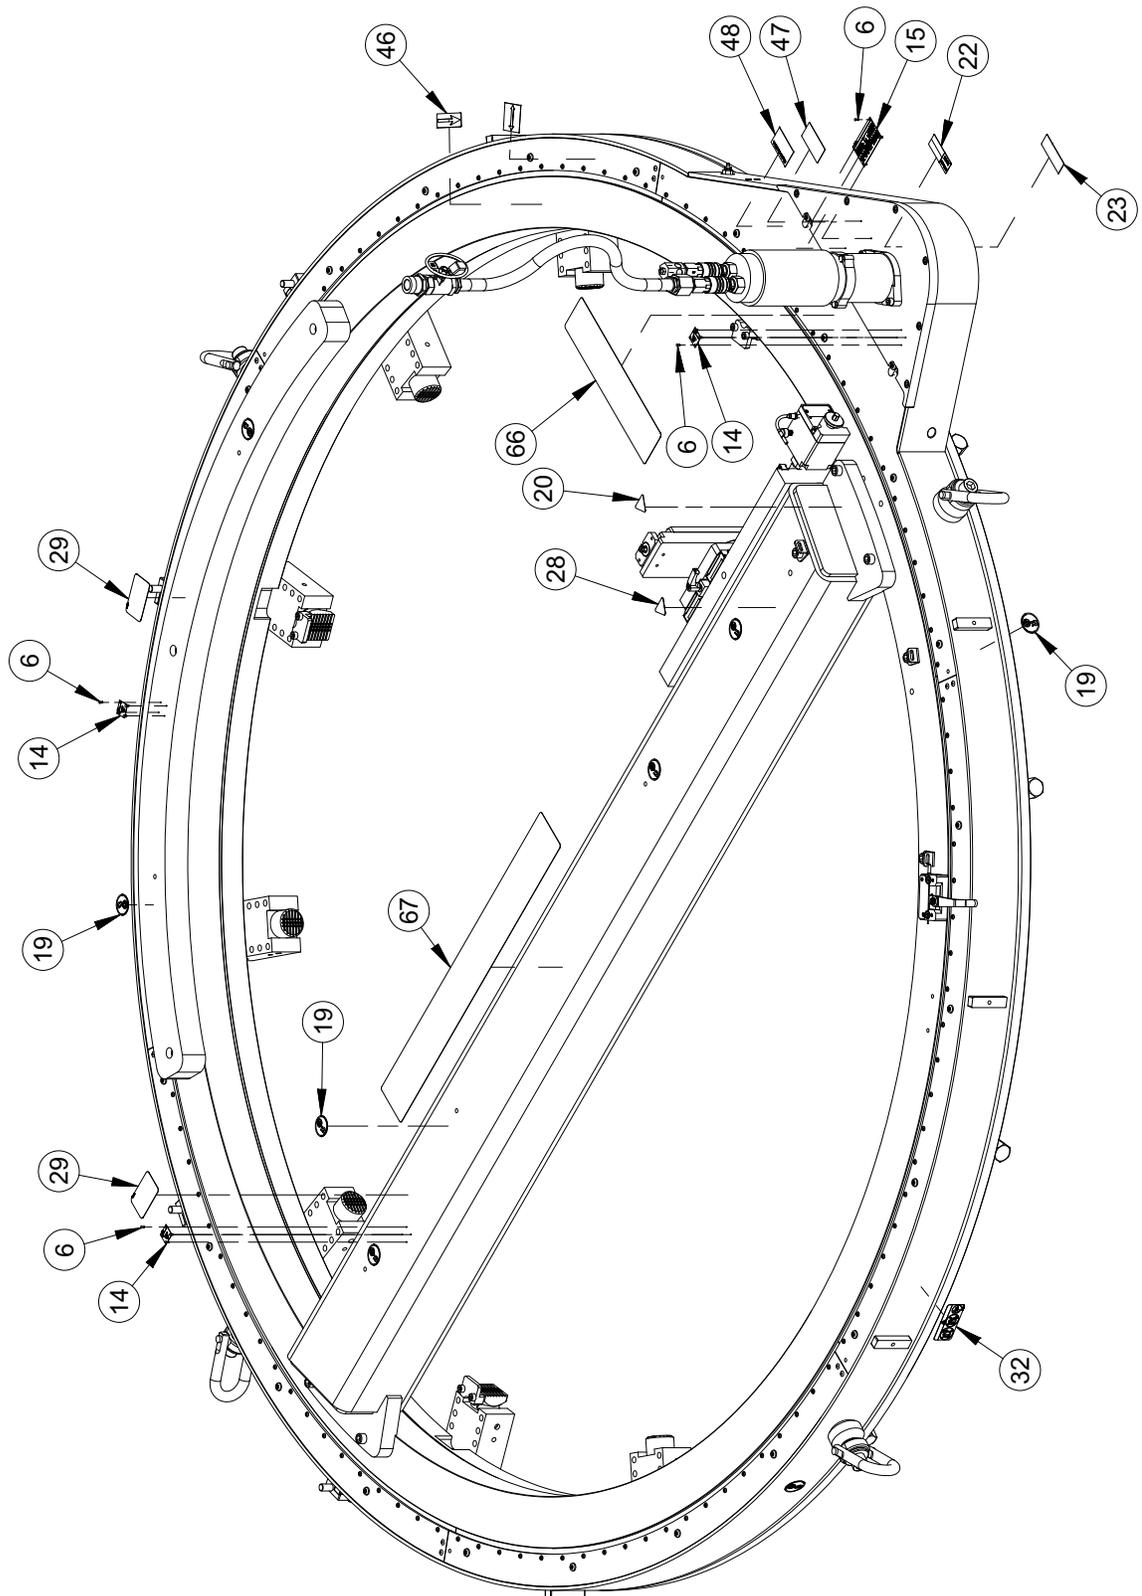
ODF90 SPEED FACER EMPLACEMENTS DES ÉTIQUETTES (RÉF. 94780)
